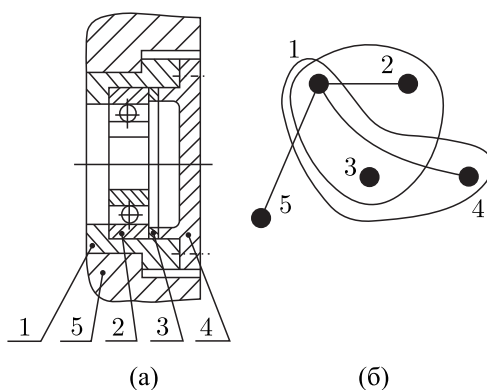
Конструкция крепления подшипника с перебазированием (а), избыточный гиперграф, описывающий механическую структуру данной конструкции (б)
